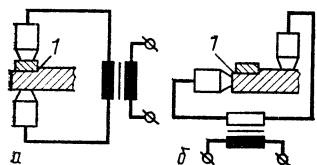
Пайка электросопротивлением: а — прямой нагрев; б — косвенный нагрев; 1 — припой
